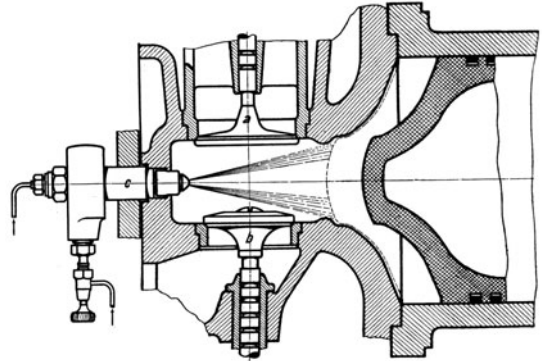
Deutzer kompressorloser Dieselmotor mit Verdrängerkolben.
